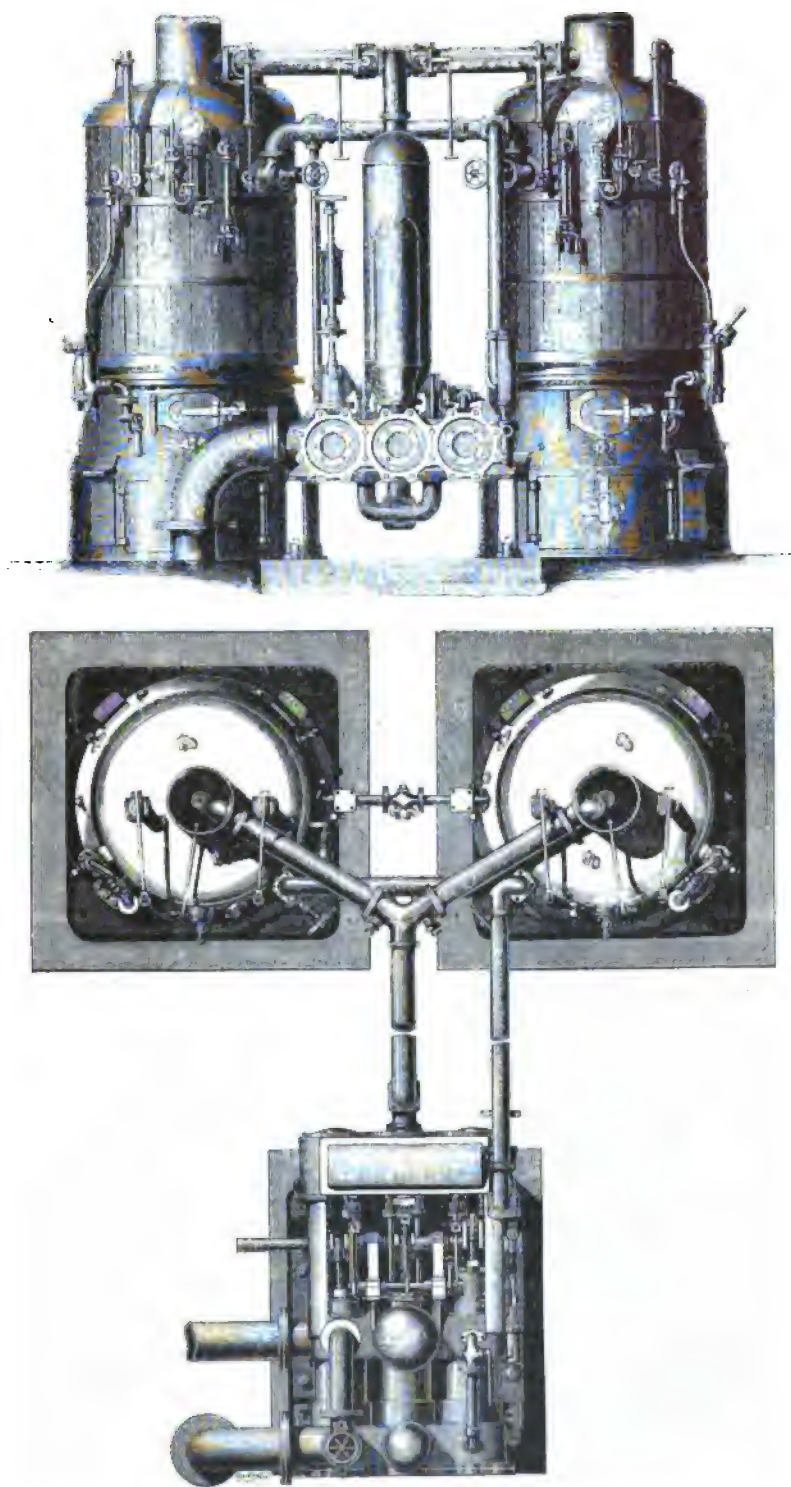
et 916. — *Shand et Mason* d'Osborne House. — Elevation et plan.
